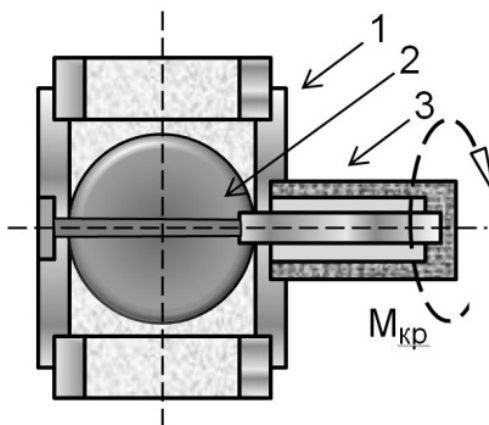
Схема превентора для нефтегазовой трубы. 1 – корпус, 2 – заслонка, 3 – актуатор кручения. [5].
